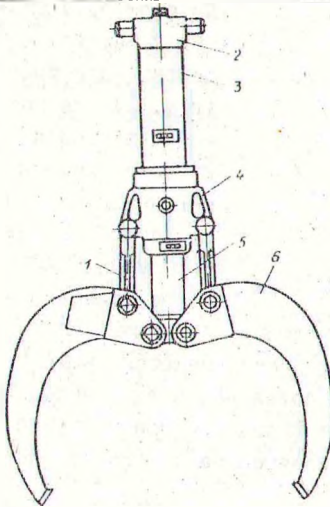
Клешевой захват манипулятора трактора для бесчелюстной трелевки: 1-рычаг; 2-траверса; 3-корпус гидроцилиндра; 4-обойма; 5-ползун; 6-клешевина.
